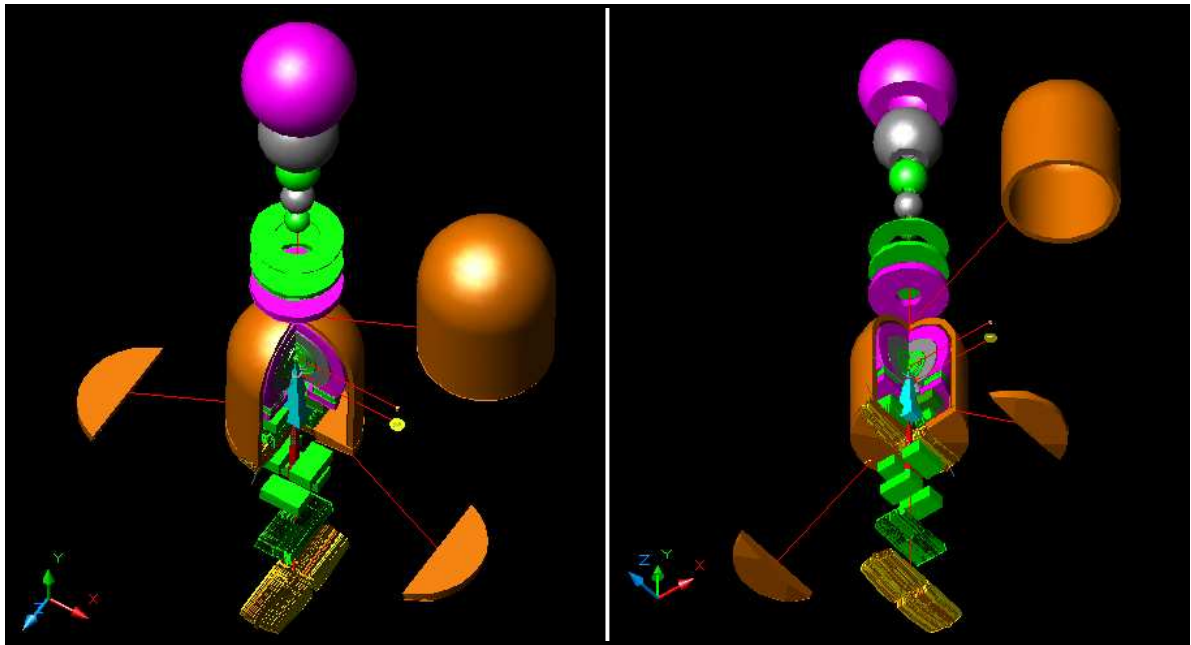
Vistas explodidas apresentando as partes internas do cabeçote e a blindagem simulada
